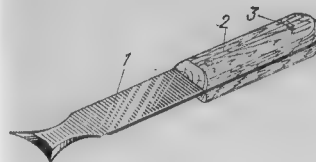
1 — лезвие; 2 — ручка; 3 — заклепка
